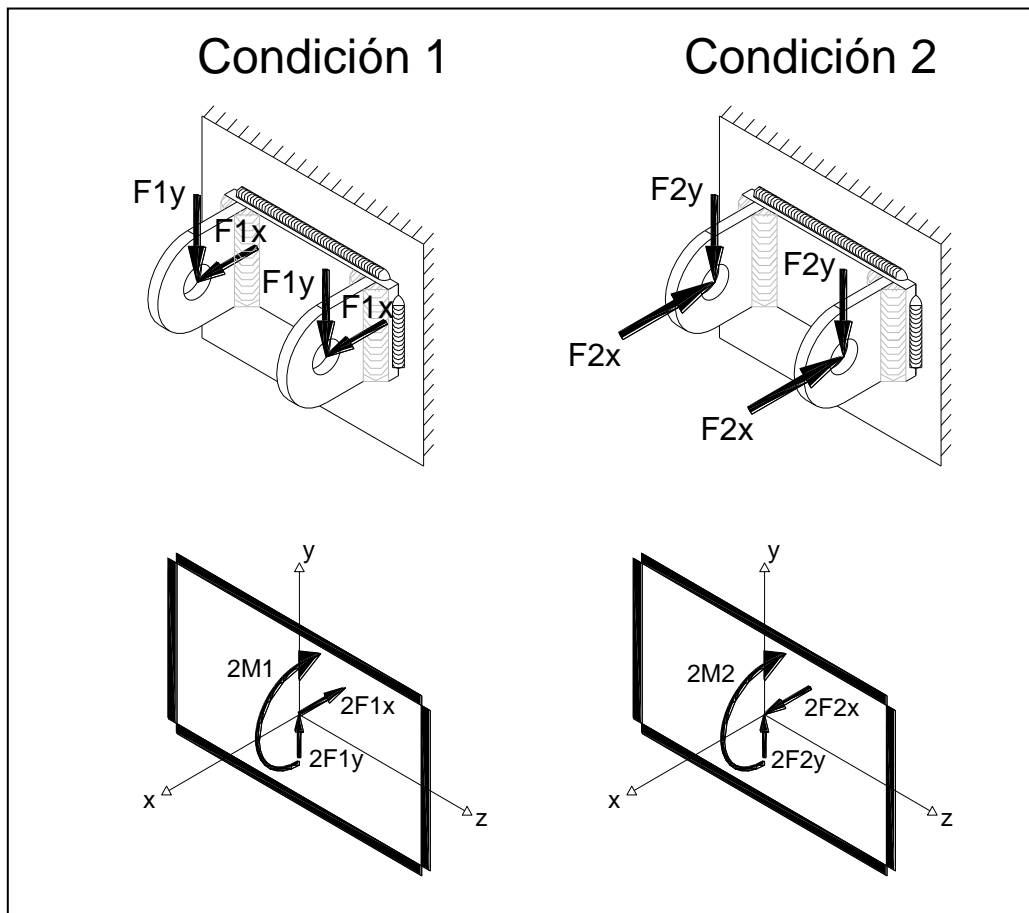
Condiciones de carga cordón soldadura anclaje inferior - Chasis
